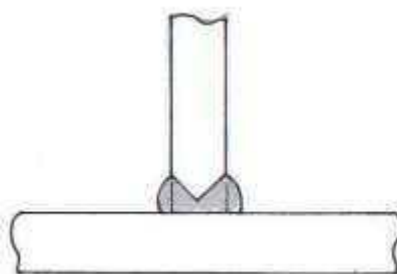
Soldadura de filete completo¹⁷
